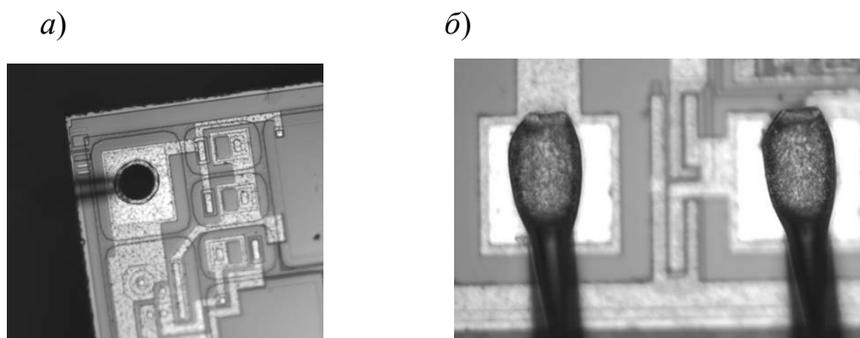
Вид сварных соединений: а – шарик на кристалле; б – клиновидная сварка на кристалле
